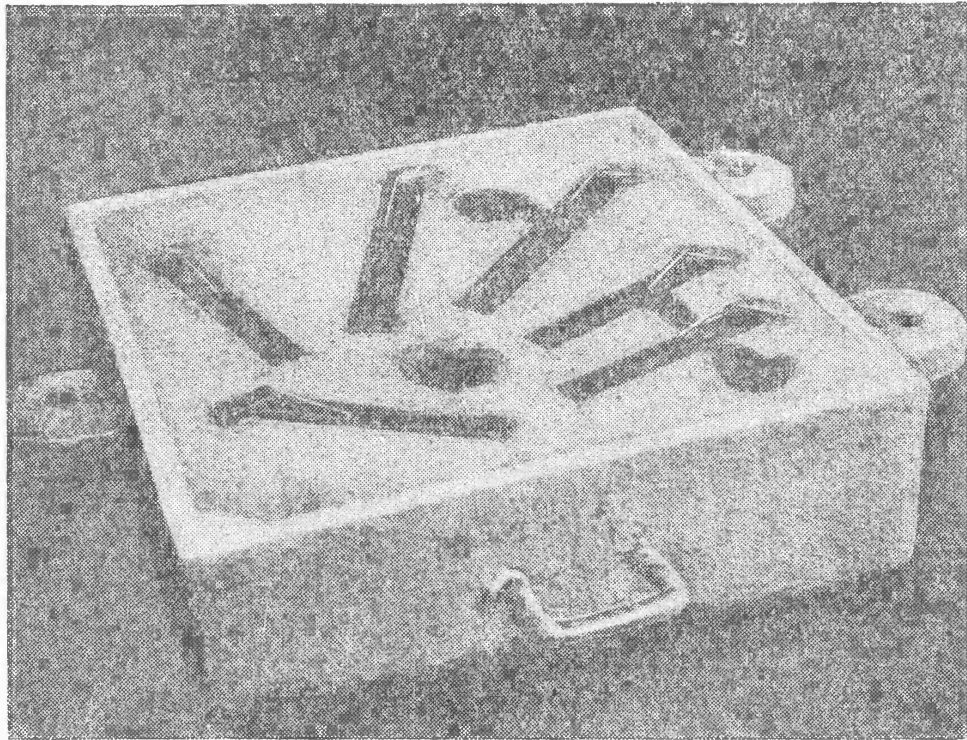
Схема формовки твердосплавных резцов с чугунными державками по способу Б. Г. Левина.
